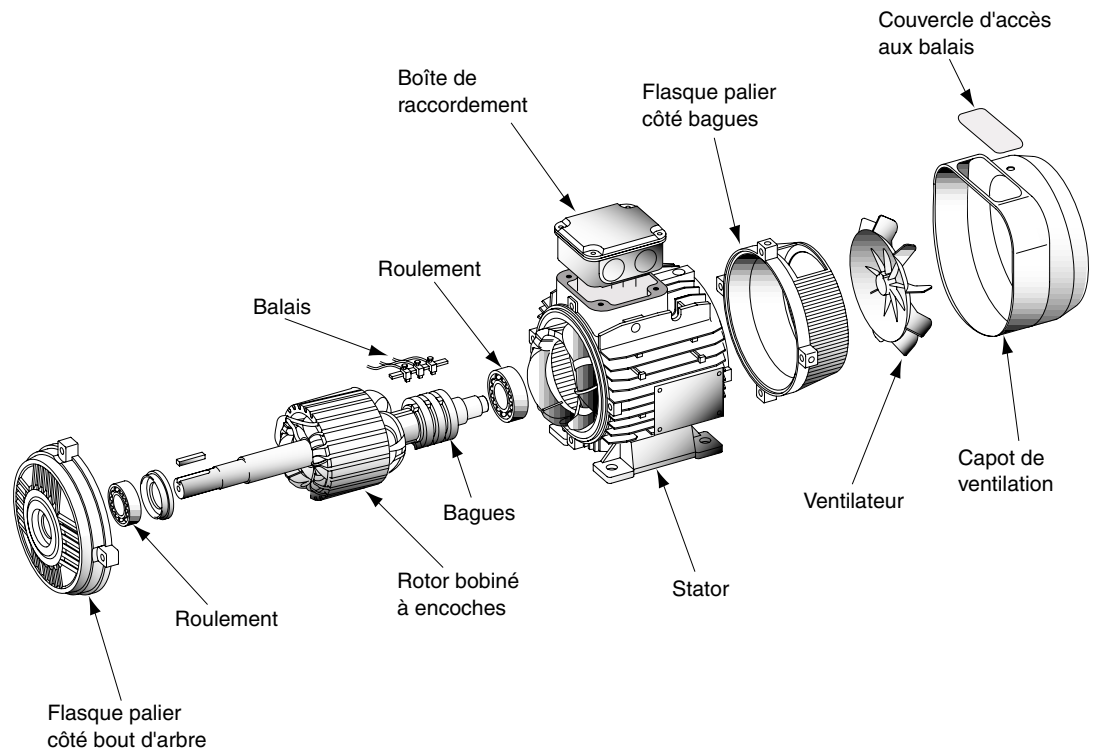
Eclaté d'un moteur à rotor à bagues.
